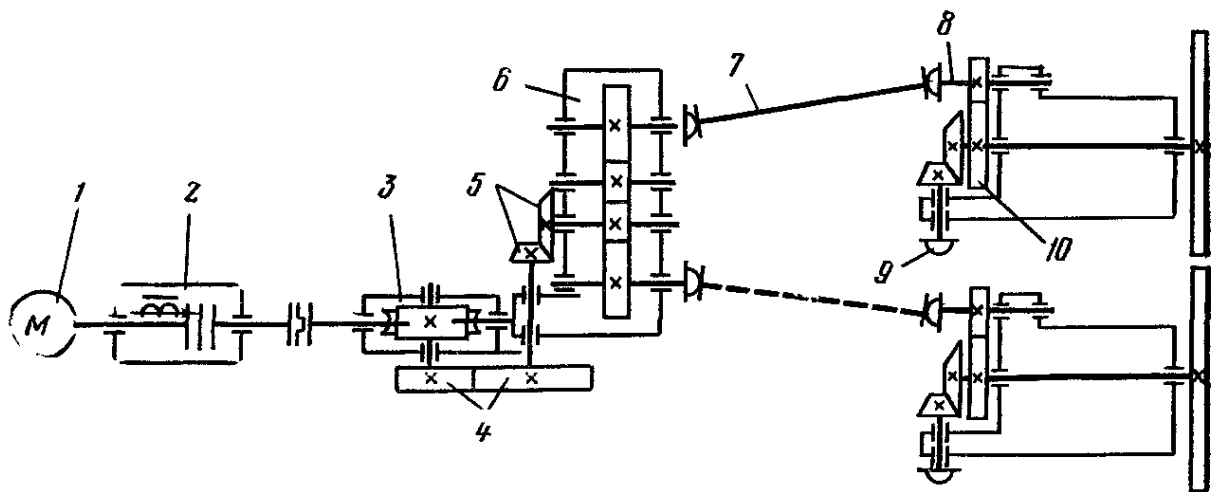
Кинематическая схема привода электродов, используемая в головке для продольной и поперечной сварки
